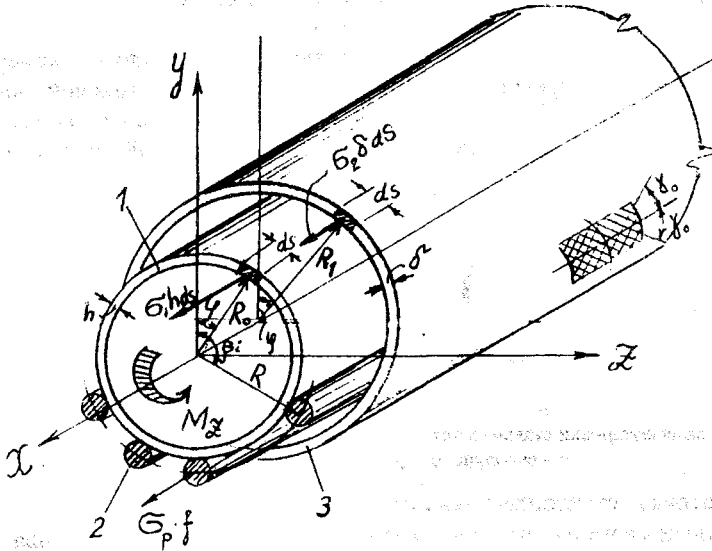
Металлостеклопластиковая труба, работающая на внутреннее давление и поперечную нагрузку:
